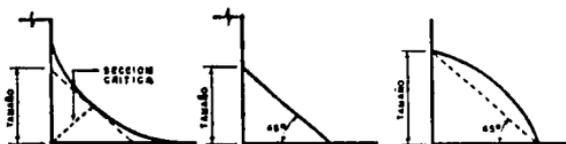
b) Perfiles deseables en soldadura de filete.
